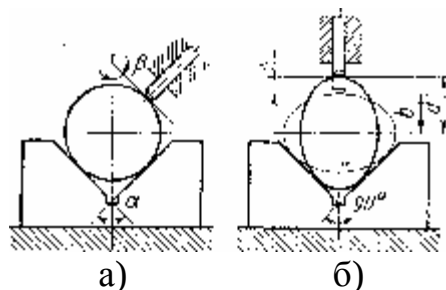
Схема контролю циліндричної деталі в призмі.
